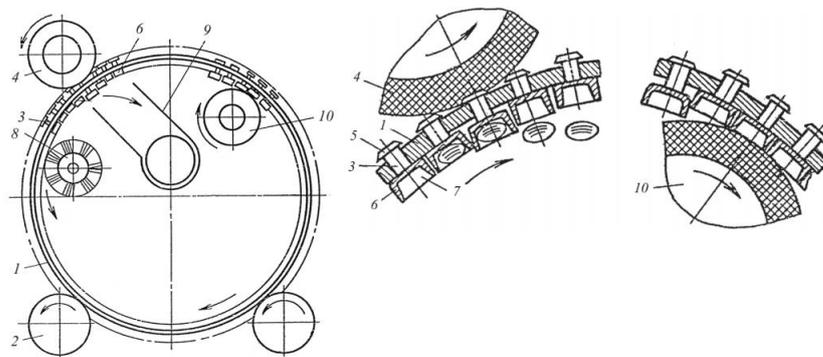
Циліндричний трієр Є.Л. Сосновського: 1 – перфорований циліндр; 2 – опорні ролики; 3 – штовхач; 4, 10 – натискні валки; 5 – зовнішній обмежувач; 6 – внутрішній обмежувач; 7 – осередки; 8 – щітки; 9 – приймальник коротких домішок.
